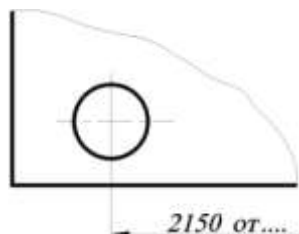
Нанесение размера от базы, не изображенной на чертеже
